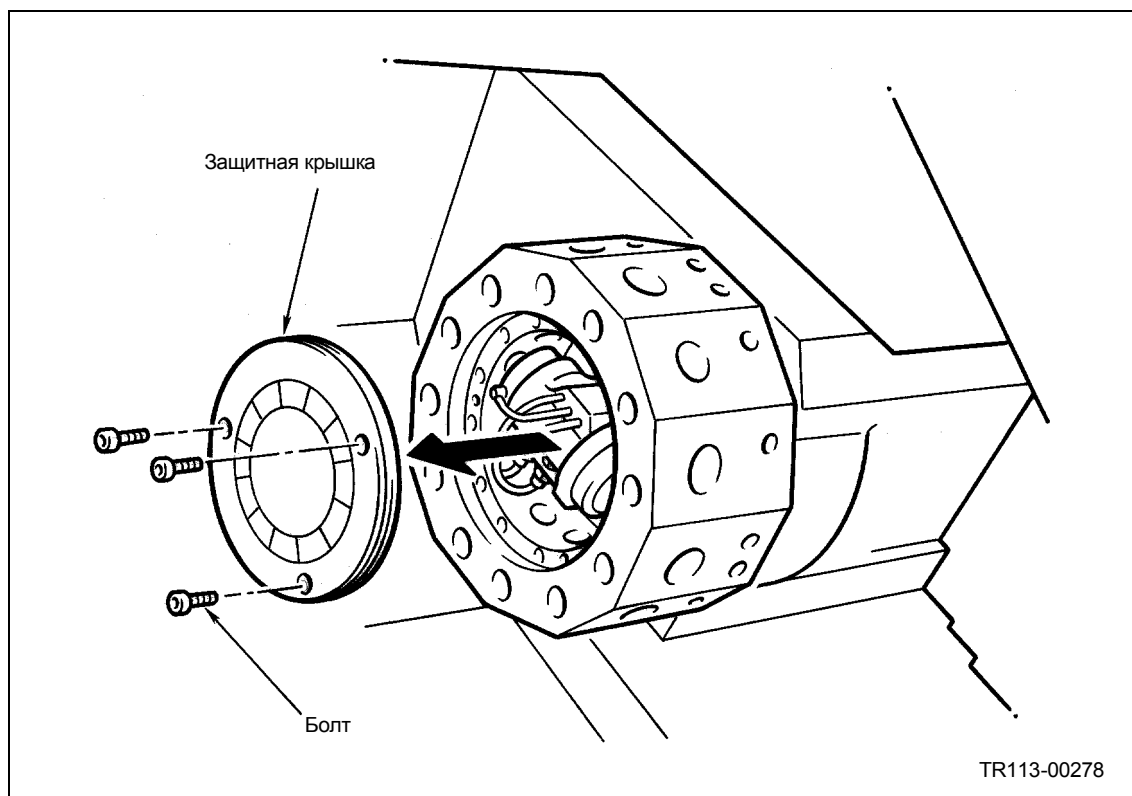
Процедура регулировки фрезерного соединения (1/2)
